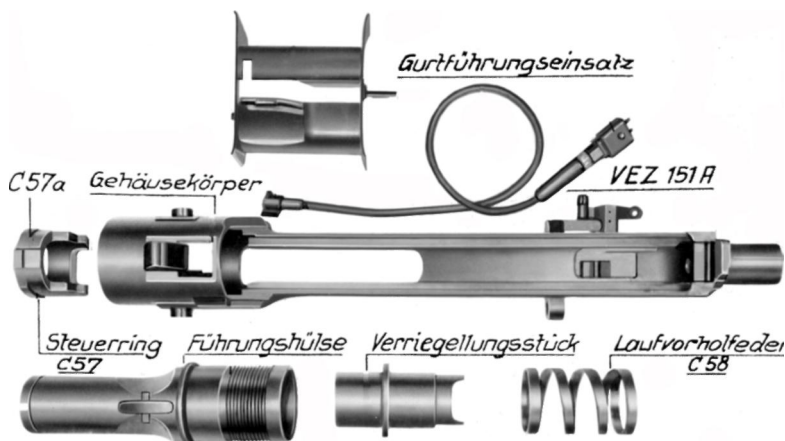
Gehäuse: Hauptteile (Ansicht von oben)
